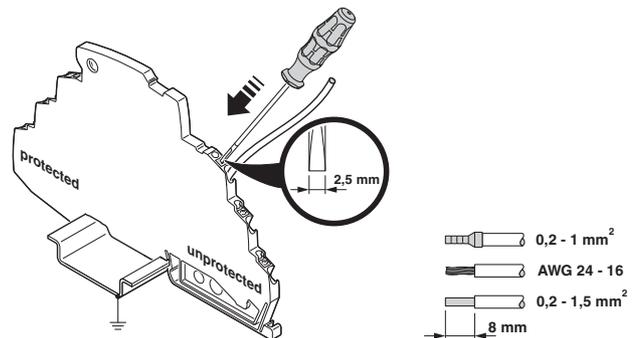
Variante de conexión push-in (ancho de construcción 3,5 mm)
